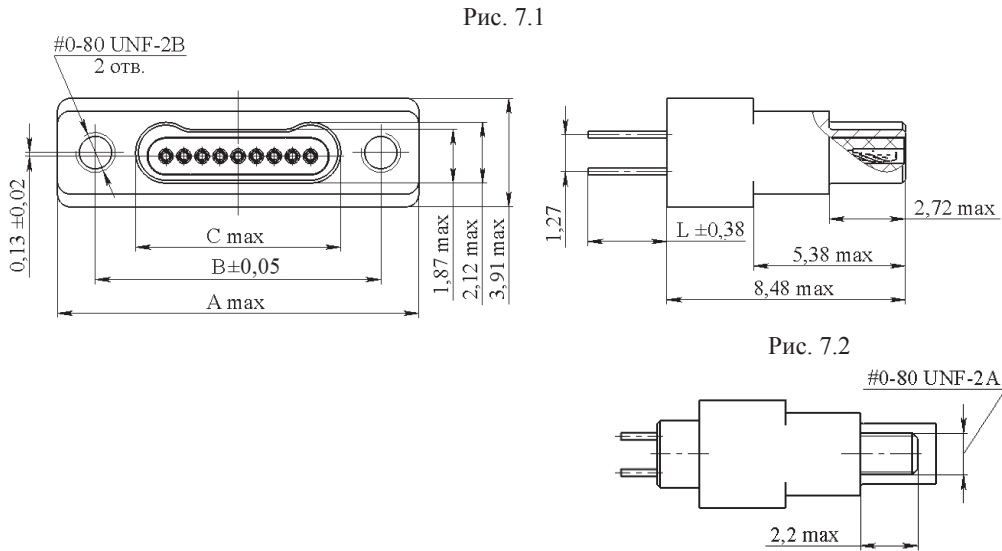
Соединитель СП450-03...1...Ш1...
